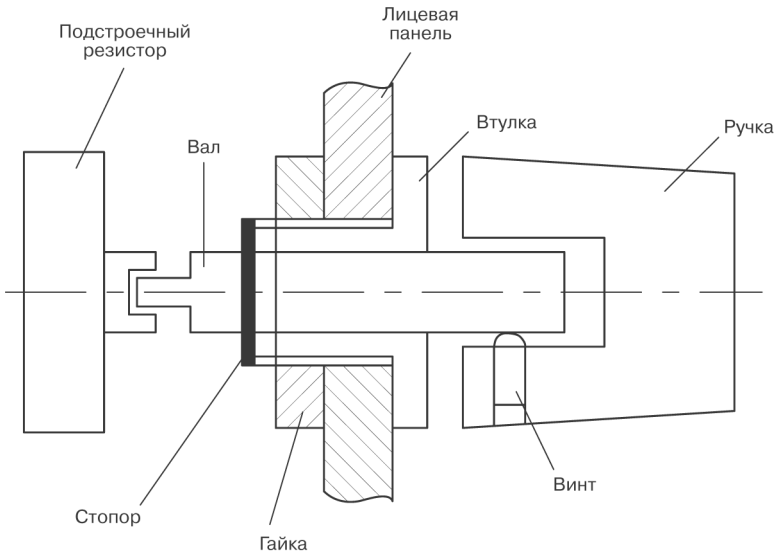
Переменный резистор, изготовленный из подстроечного
